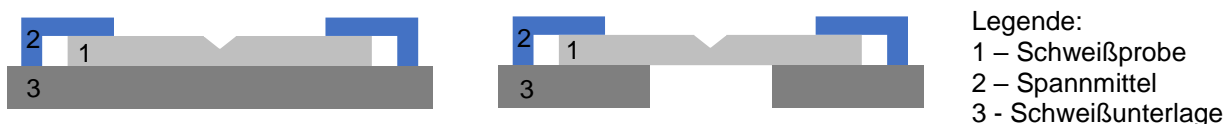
Aufspannung des Probebleches auf einer durchgängigen Schweißunterlage (links) und einer geteilten Schweißunterlage (rechts)
